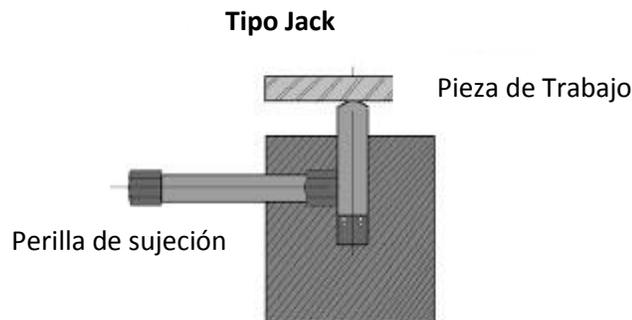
Pin tipo Jack. Fuente: American Machinist
